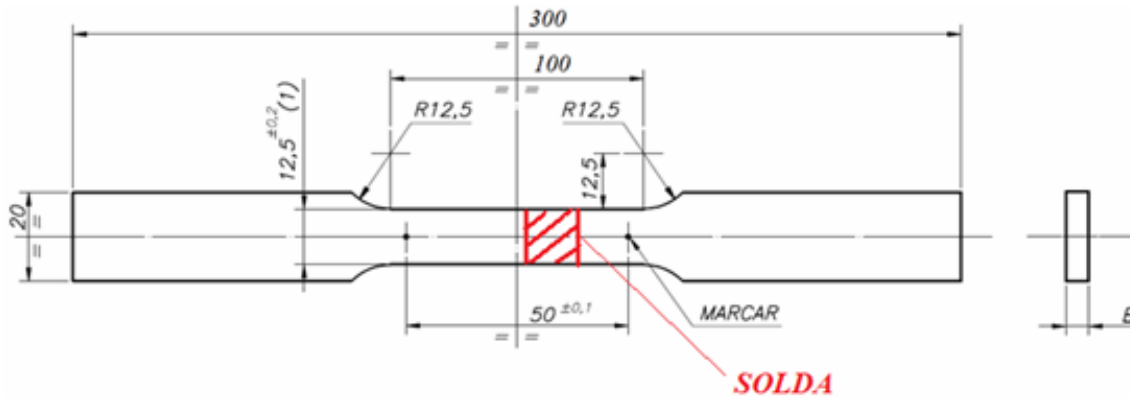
Corpo de prova de tração e posição da solda com chanfro meio-V. Dimensões em mm. E = 5 mm.
